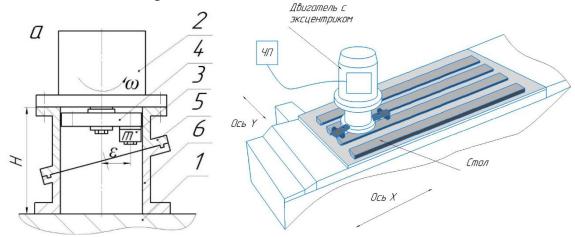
Конструкция источника вынужденных колебаний и схема расположения источника вынужденных колебаний при нагружении вибрацией подвижного стола фрезерного станка
